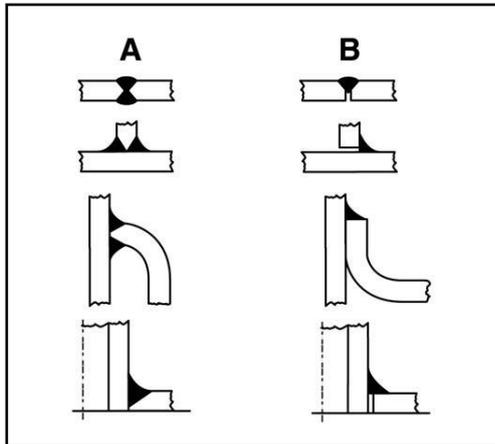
Ejemplos de realización de uniones soldadas
